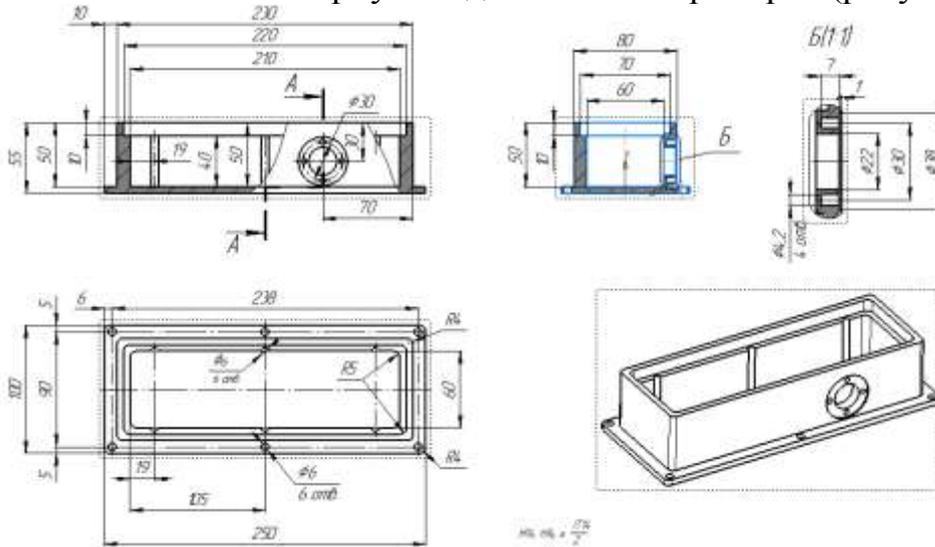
Фрагмент чертежа корпуса элемента геодезического комплекса
